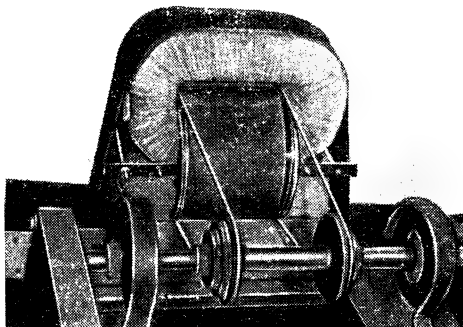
Станочное приспособление конструкции инж. А. И. Фролова для вматывания обмоток в замкнутые сердечники МУ.
